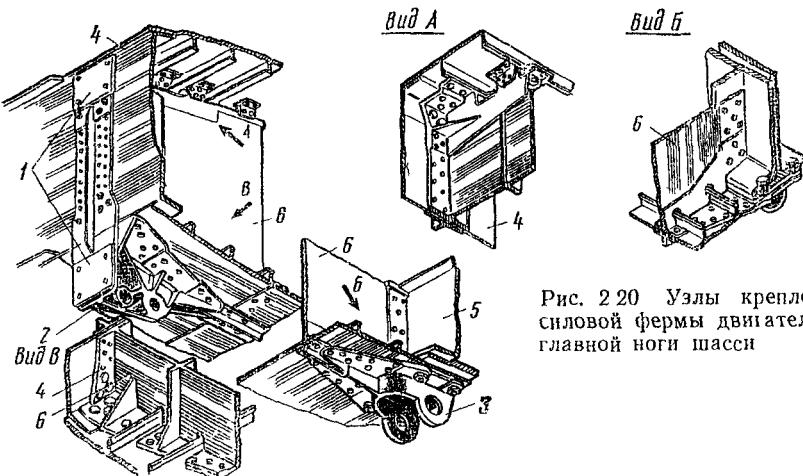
Узлы крепления силовой фермы двигателя и главной ноги шасси
